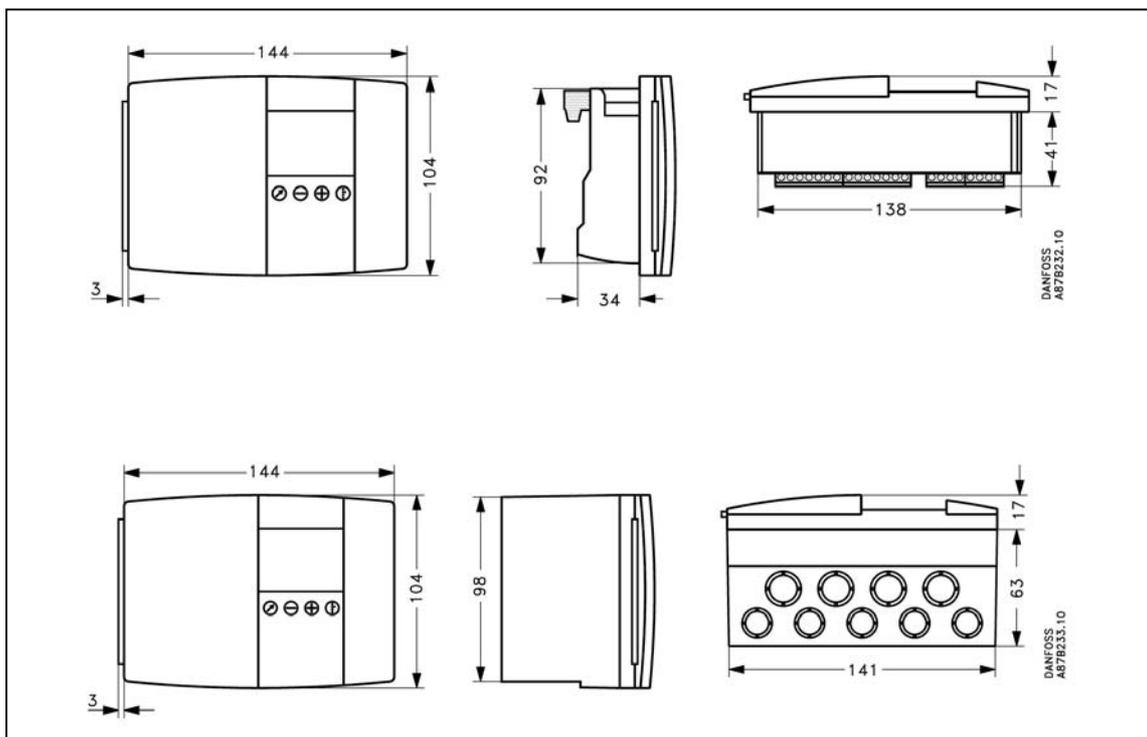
Габаритные и присоединительные размеры электронного регулятора ECL 300.
